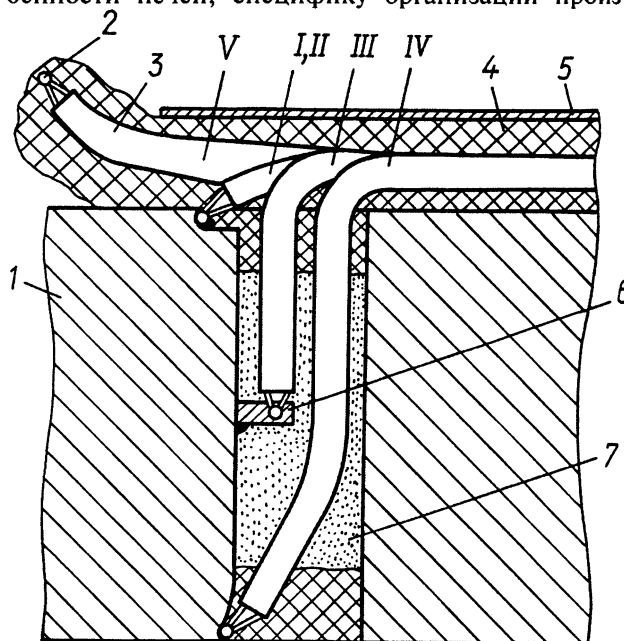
Схема установки и закрепления термодатчиков: 1 – заготовка; 2 – спай термодатчика; 3 – двухканальная алюминиевая соломка; 4 – каолиновая вата; 5 – уголок или тавр; 6 – планка; 7 – безводный оксид алюминия; I, II – термопары, измеряющие температуры грани и угла (верхняя поверхность); III – центр; IV – грань (нижняя поверхность); V – температура среды
